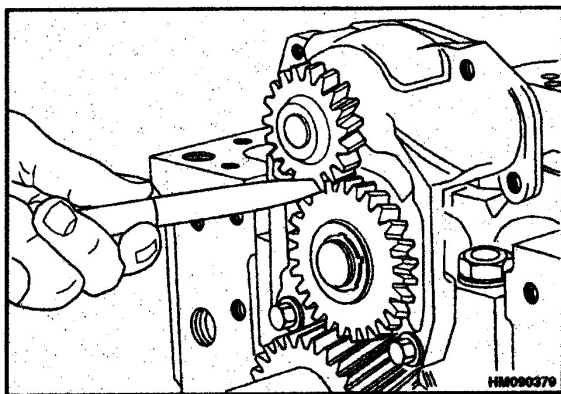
Проверка зазоров между шестерней масляного насоса и промежуточной шестерней.
